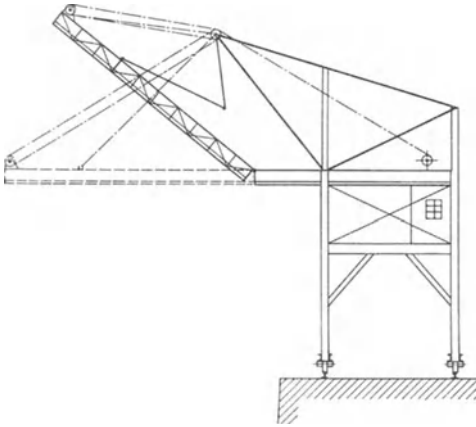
Uferkran mit großer einseitiger Ausladung. Benrather Maschinenfabrik.
